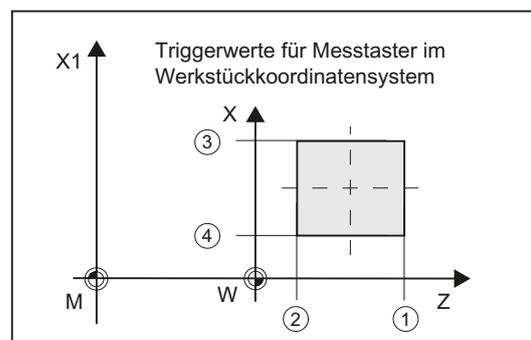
Werkzeugmesstaster, werkstückbezogen (G18)
